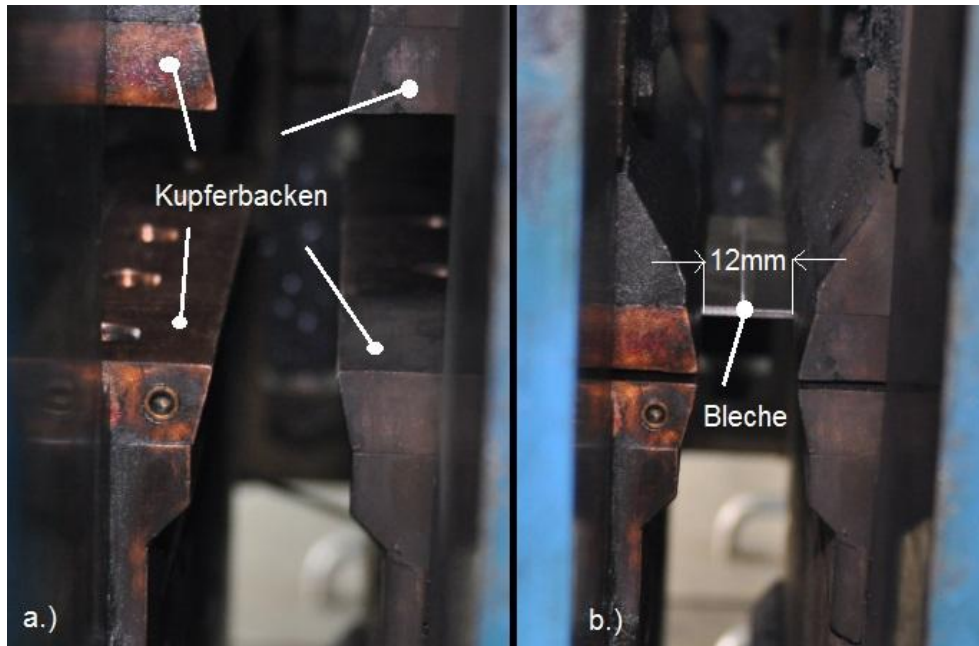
Presstumpfschweißversuch auf einer Ideal AS 100S PS/ABS Schweißanlage; a – Kupferbacken; b – freie Einspannlänge der zu schweißenden Bleche.
